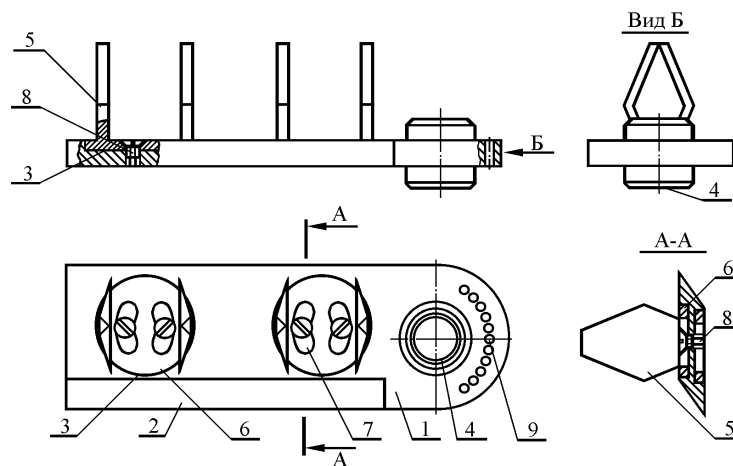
Разрушающий элемент измельчителя-смесителя кормов:
